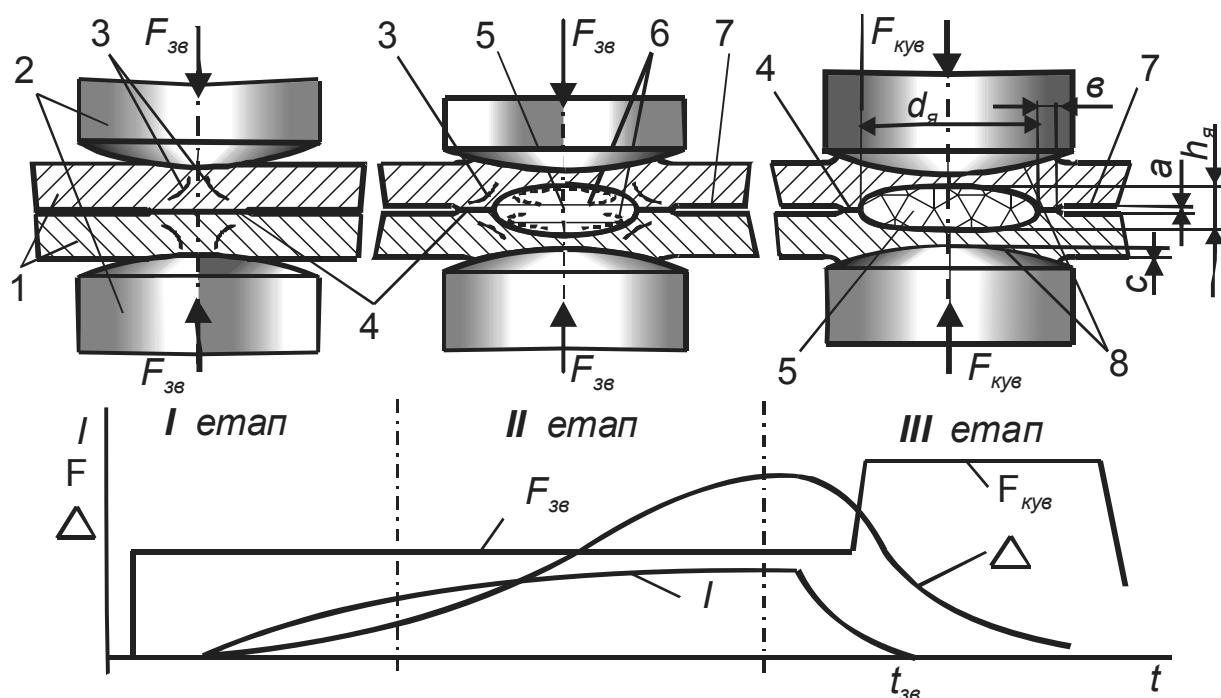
Етапи утворення з'єднання при точковому зварюванні
